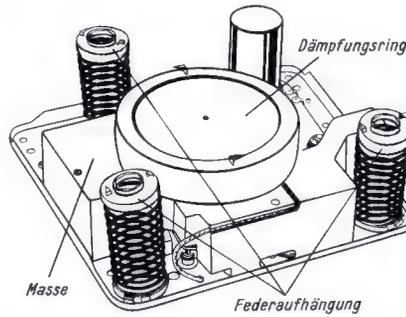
Chassisaufhängung des Auto-Mignon an drei Druckfedern
